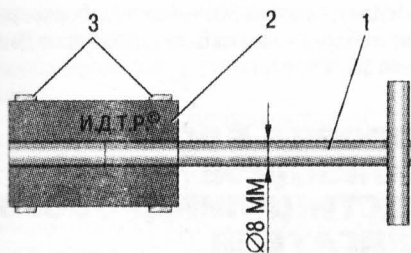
Приспособление для притирки клапанов: 1 – металлический стержень; 2 – резиновый шланг; 3 – винтовой хомут
